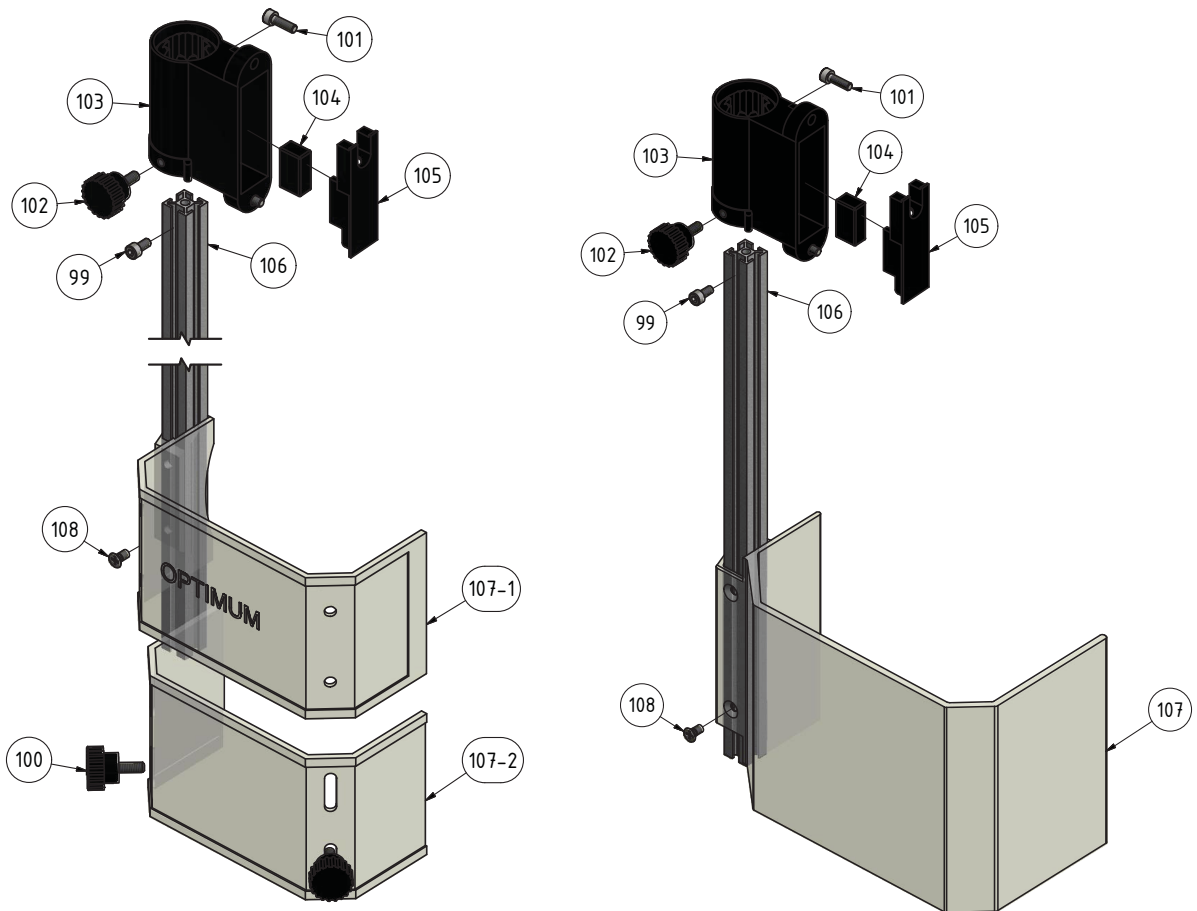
Bohrfutterschutz- Drilling chuck protection
